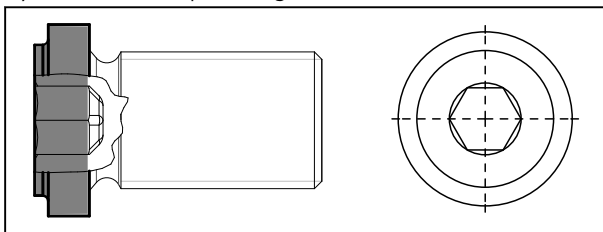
Der Schraubenkopf hat zwei Stufen.
